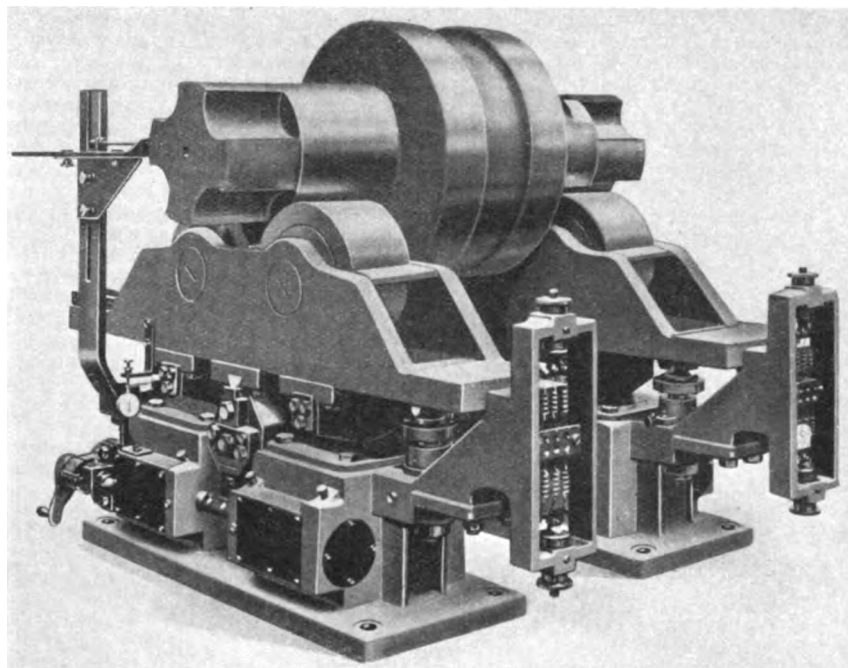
Wuchtmachine ET, für Prüfkörper von etwa 1000 ... 75 000 kg Gewicht.
